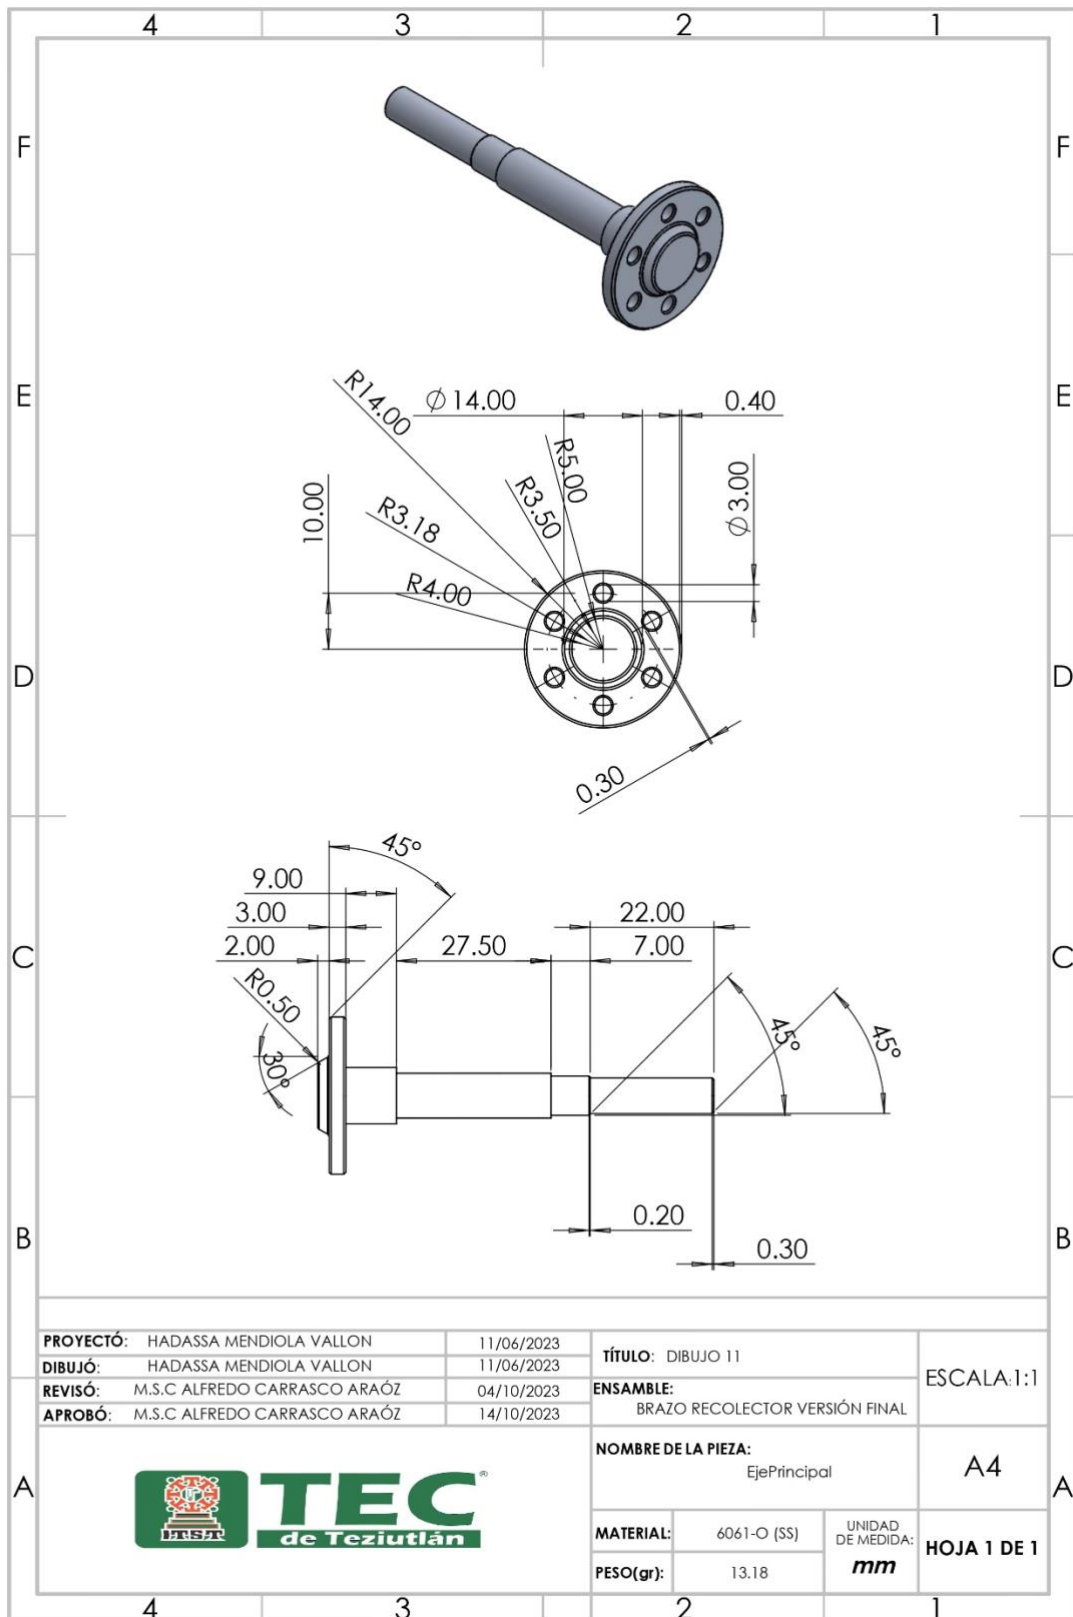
Dibujo en SolidWorks "Eje Principal". Autor propio
